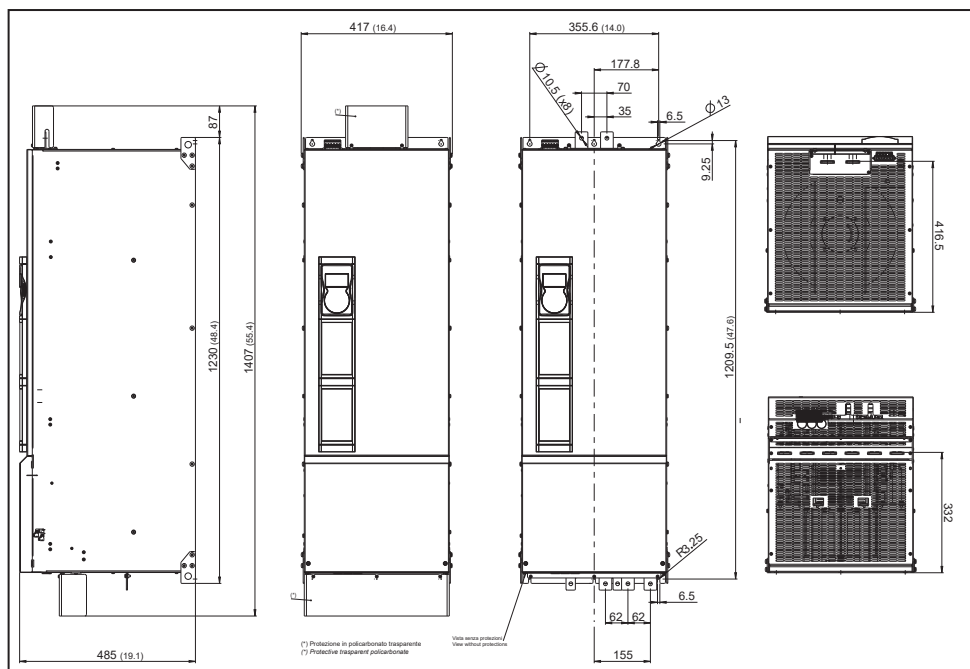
Dimensioni FFE200-550...880-4 e FFE200-500...760-6
